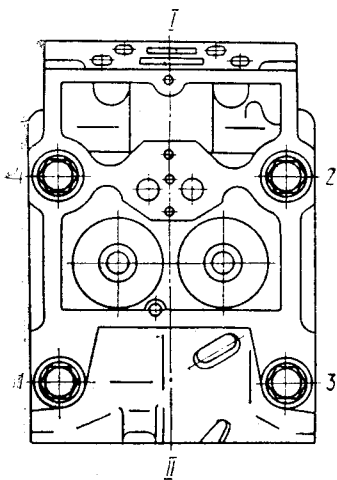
Порядок затяжки болтів кріплення головки циліндра двигуна КаМАЗ-740:
